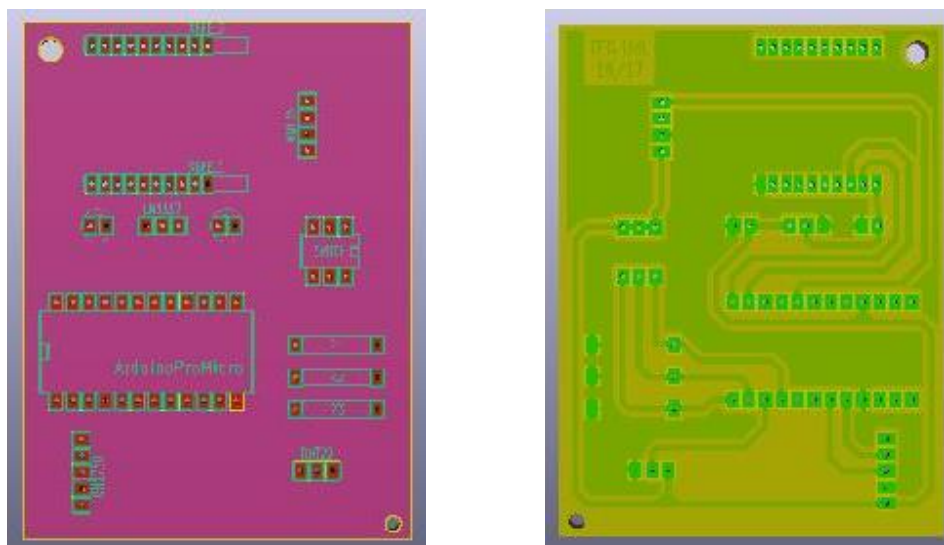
Disseny final de la placa PCB en 3D de les dues cares
